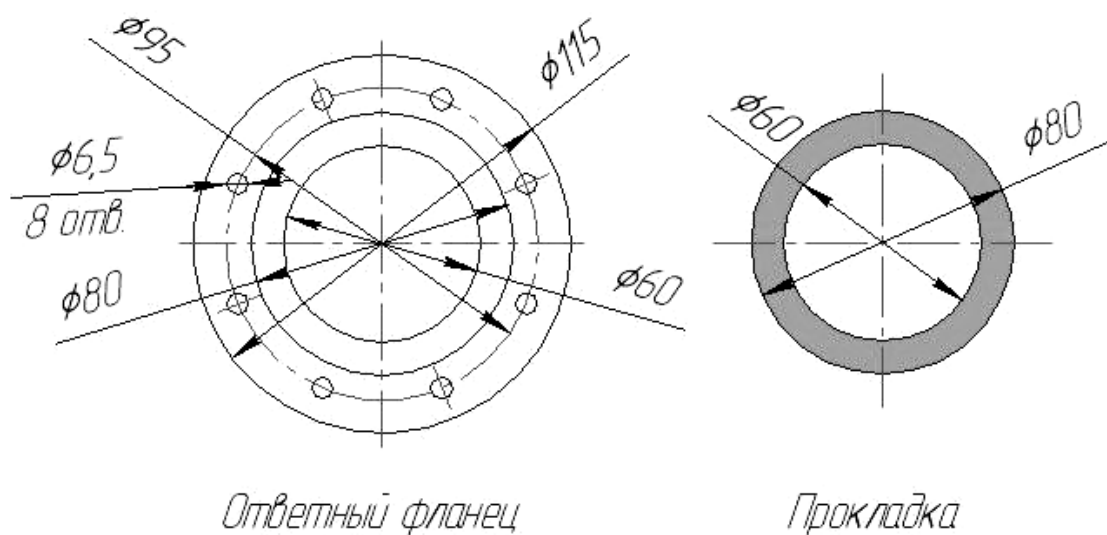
Габаритные размеры установочного фланца и прокладки для сигнализаторов
